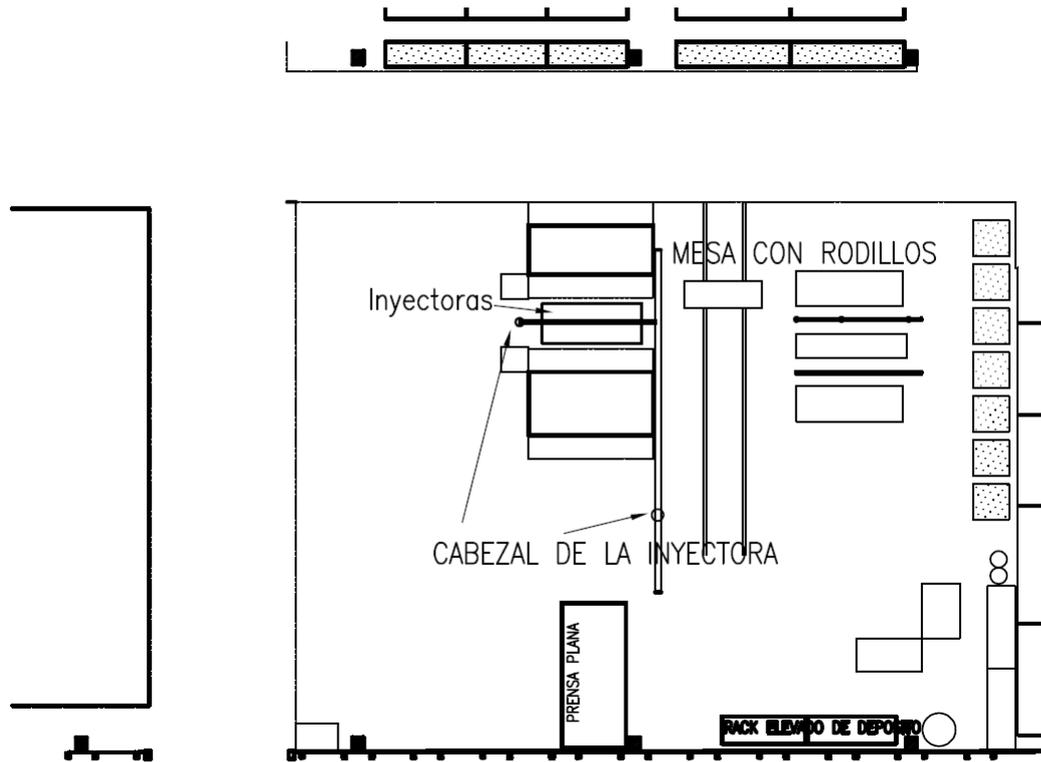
Vista en planta del sector de espumado con las inyectoras entre las prensas.
